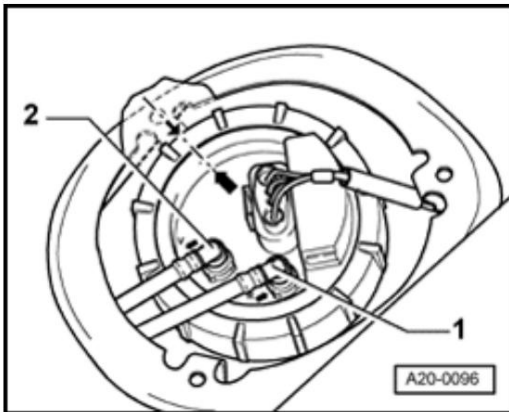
Posición instalada de la brida de la unidad de suministro de combustible
